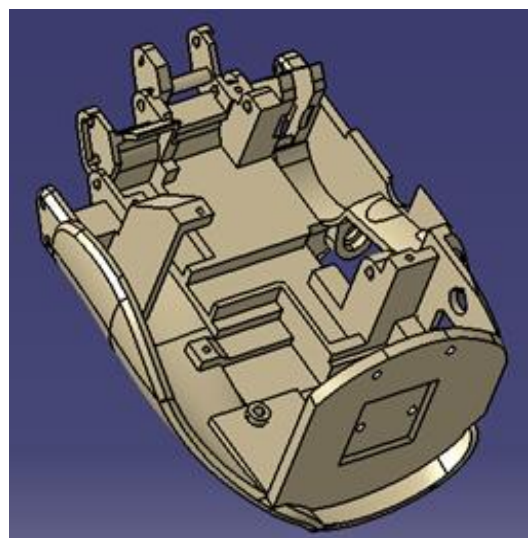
Recorte del archivo CAD del subconjunto del pulgar de la mano Hackberry.
